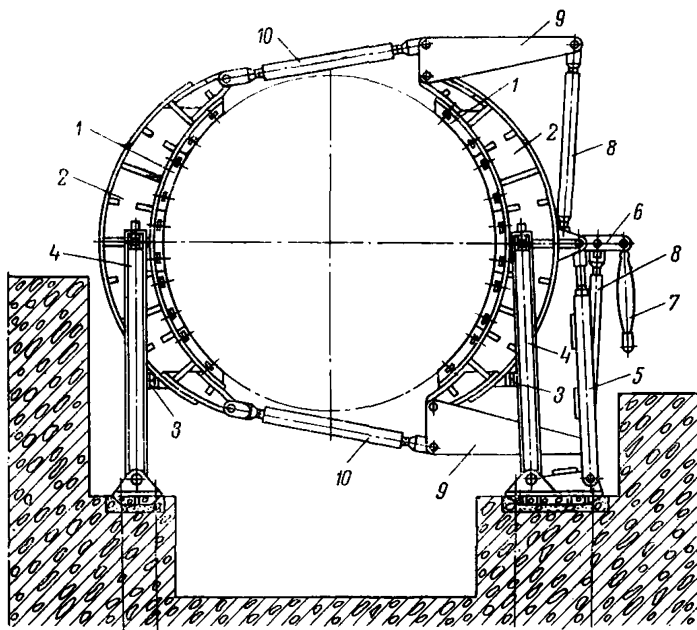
Исполнительный орган тормоза с параллельным перемещением колодок и передним расположением регулировочной стойки:
